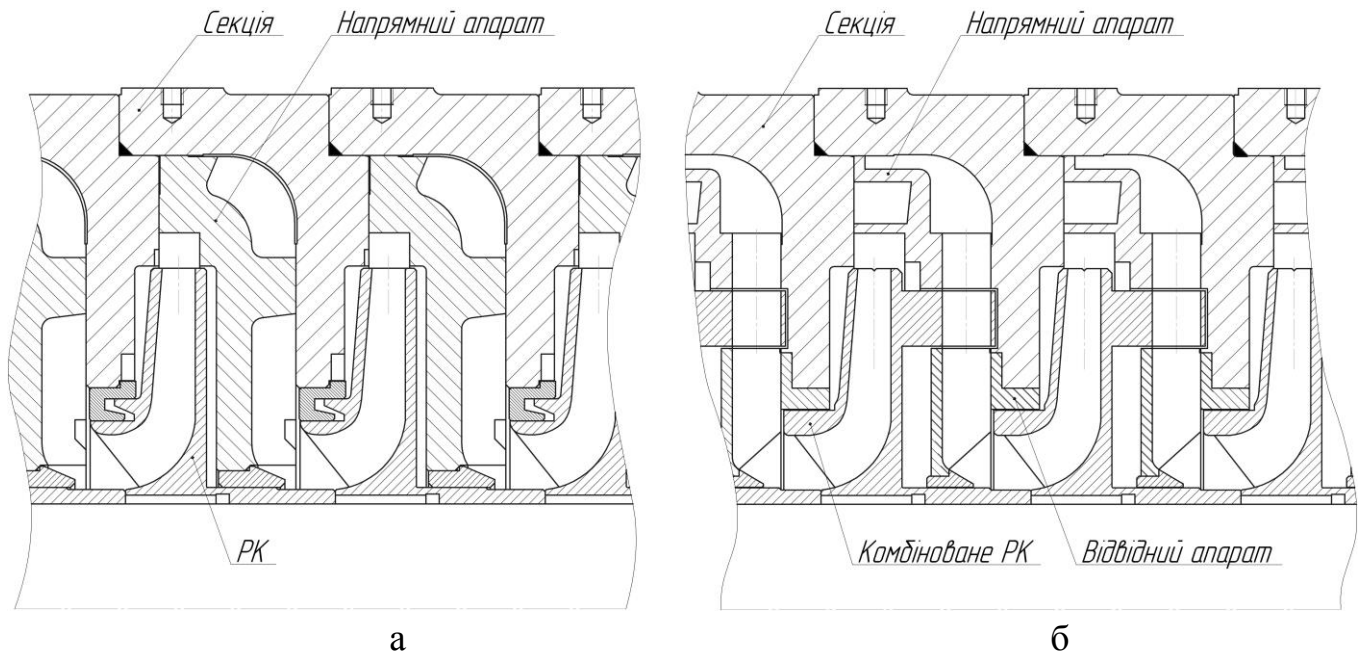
Переріз проточної частини багатоступеневого насоса: а – стандартна відцентрова; б – комбінована відцентрово-доцентрова; РК – робоче колесо
